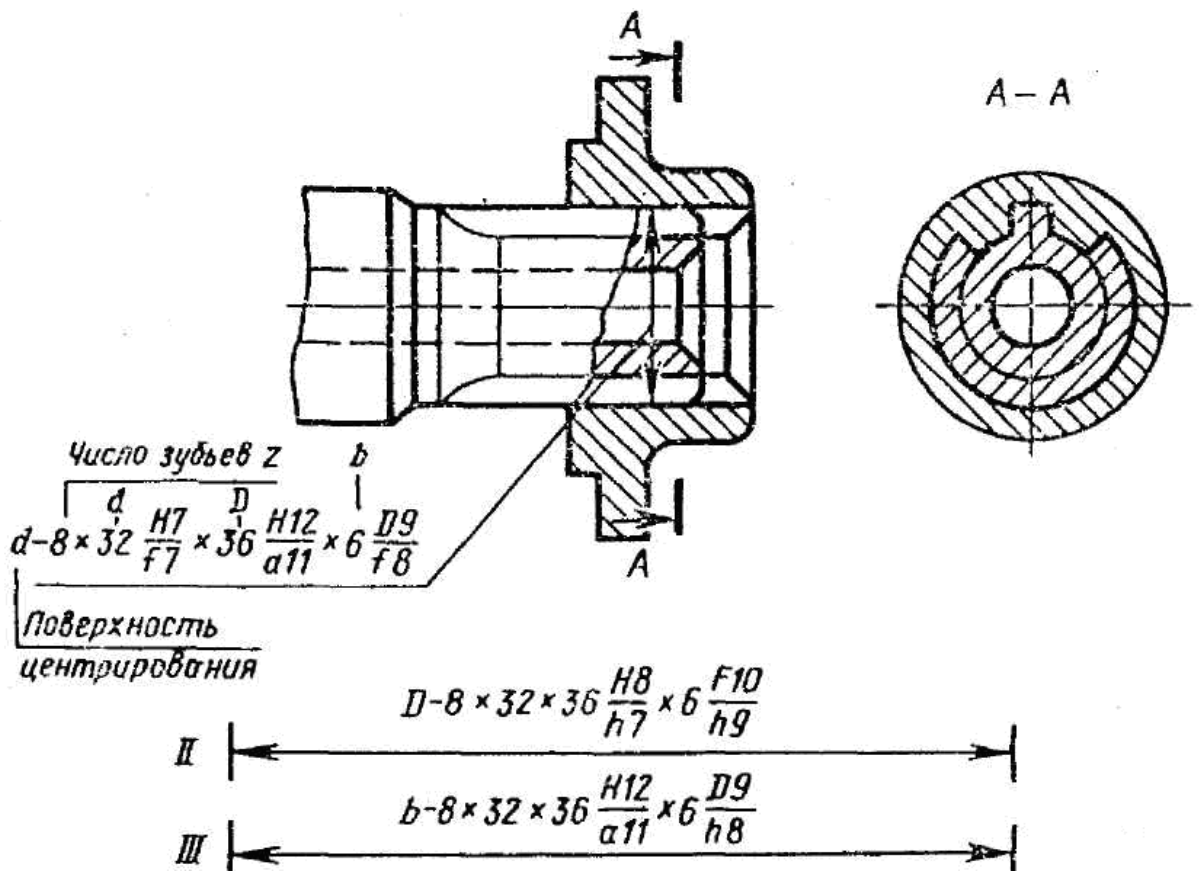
Обозначение допусков и посадок прямобочного шлицевого соединения на сборочном чертеже
